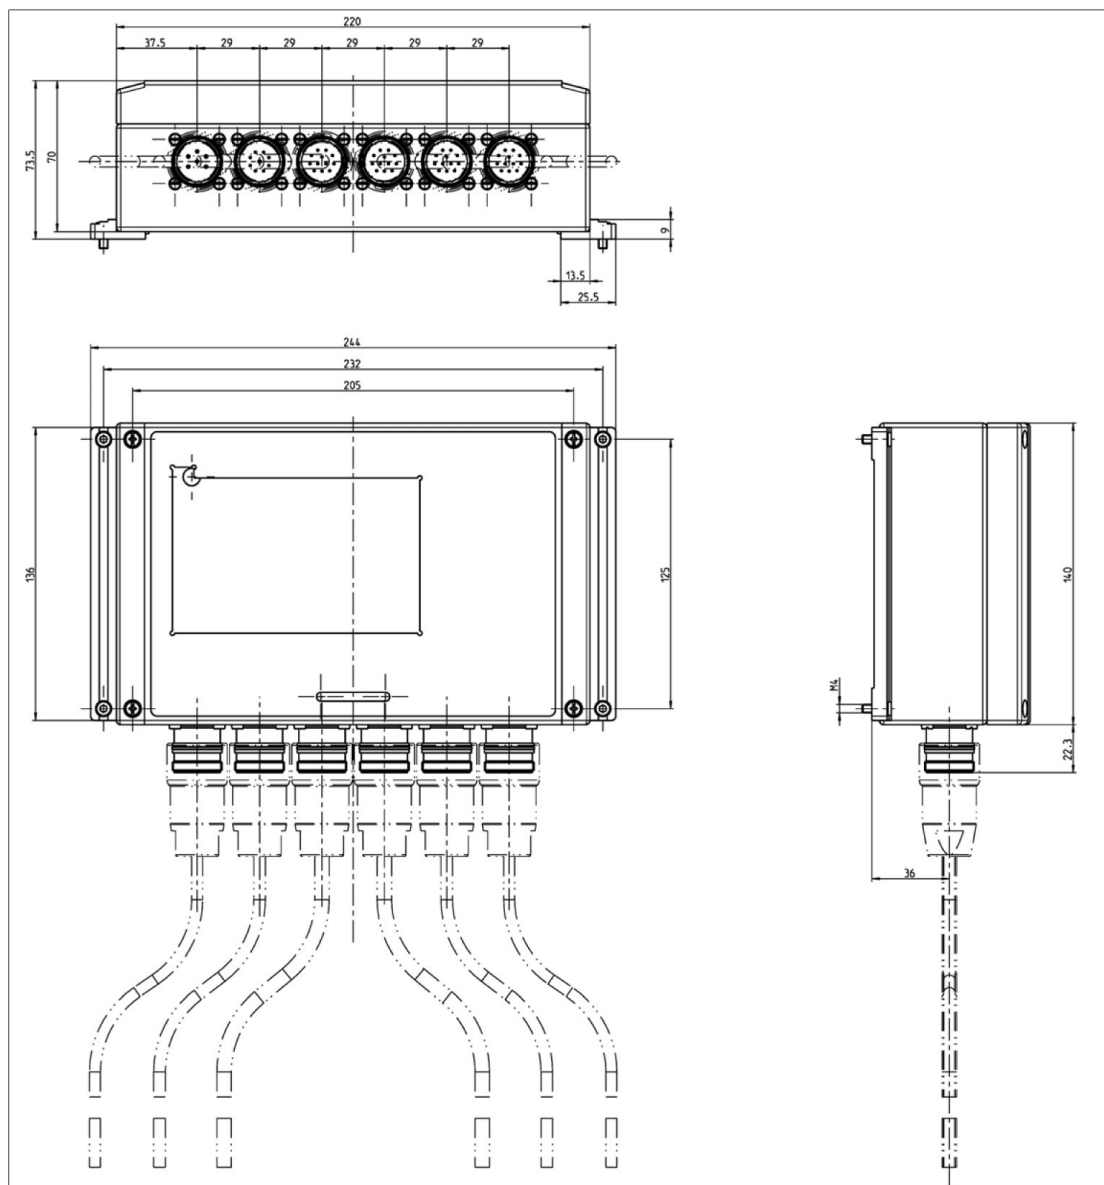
Dimensiones del evaluador SiCOMS®
